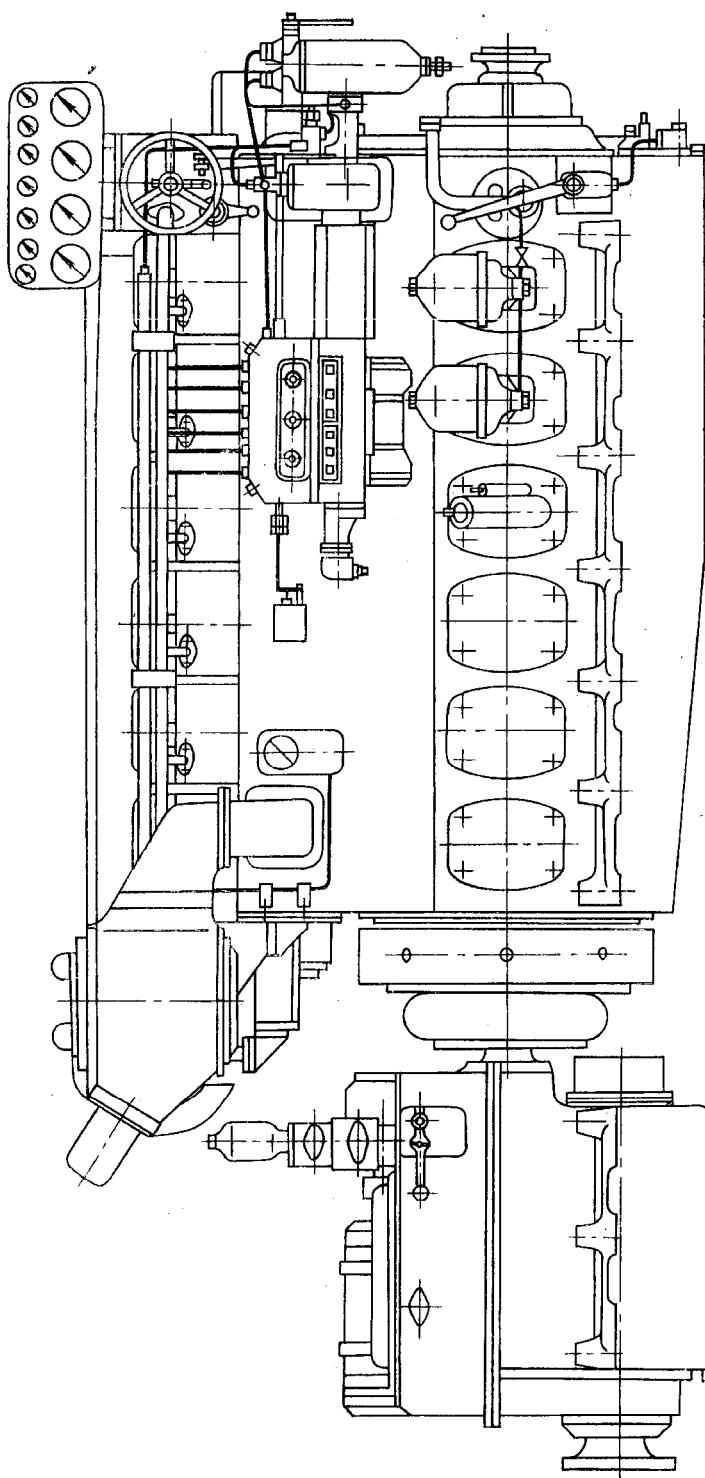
Общий вид дизель-редукторного агрегата 6CSPN2A18/22-315 (ДД 107)
